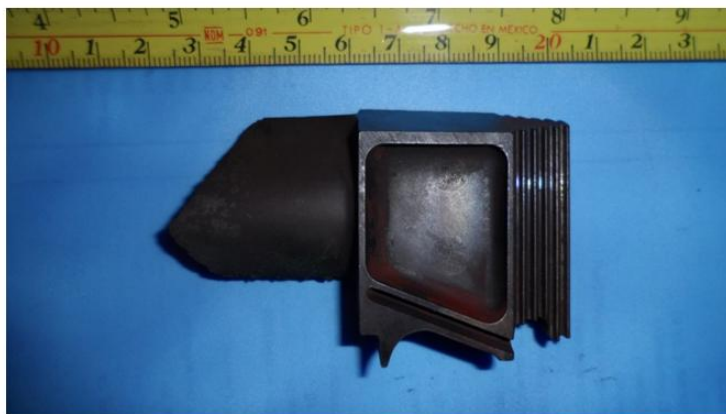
Álabe fracturado de una turbina industrial.
